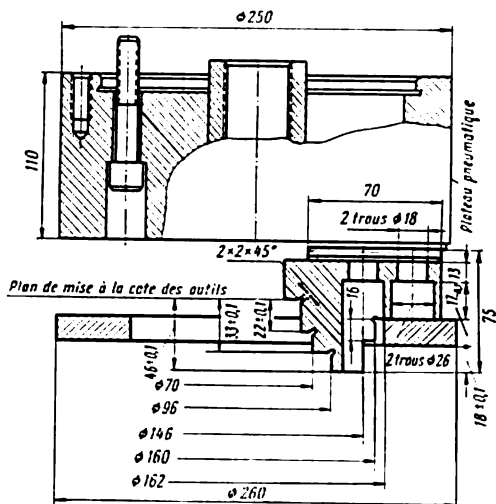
Mors de mandrin pour la mise en place successive de plusieurs pièces avec réglage de groupe de la machine-outil
